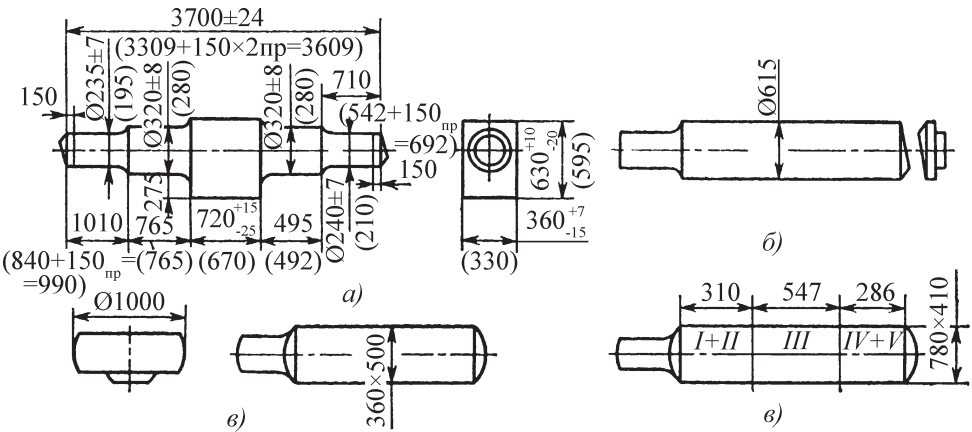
Поковка (а) и переходы ковки (б–г) коленчатого вала
